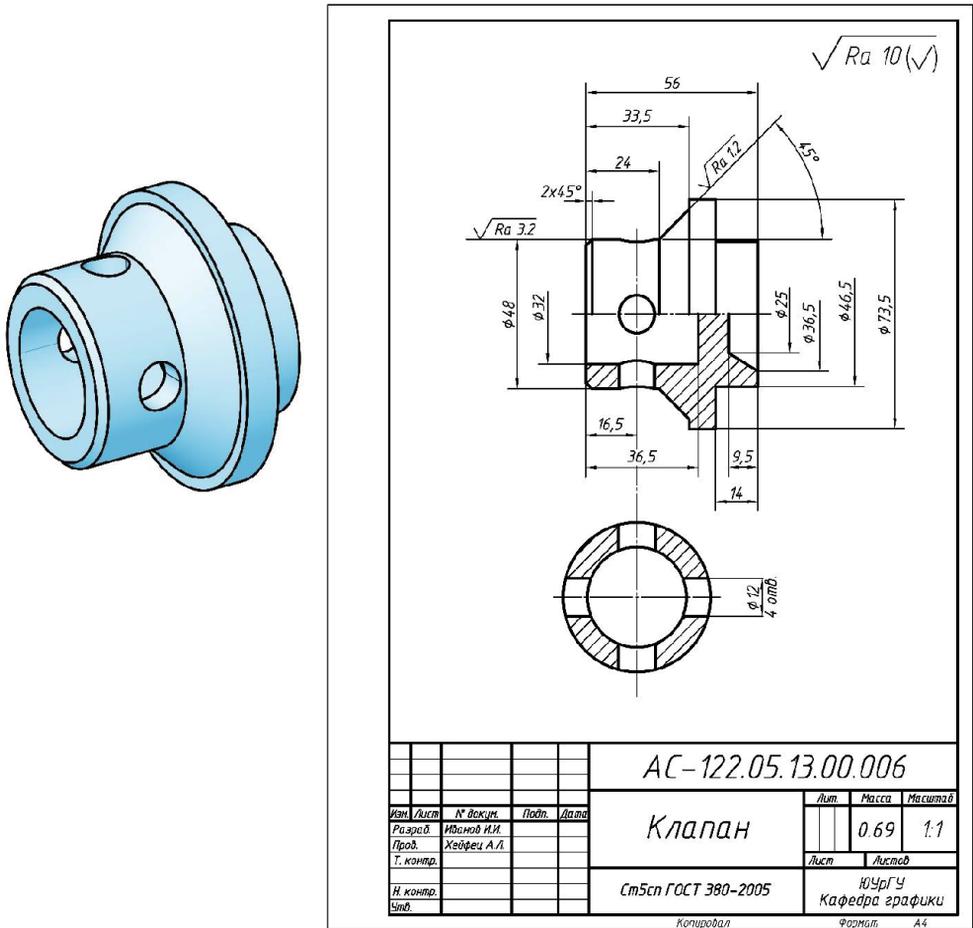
Модель и рабочий чертеж детали «клапан»
